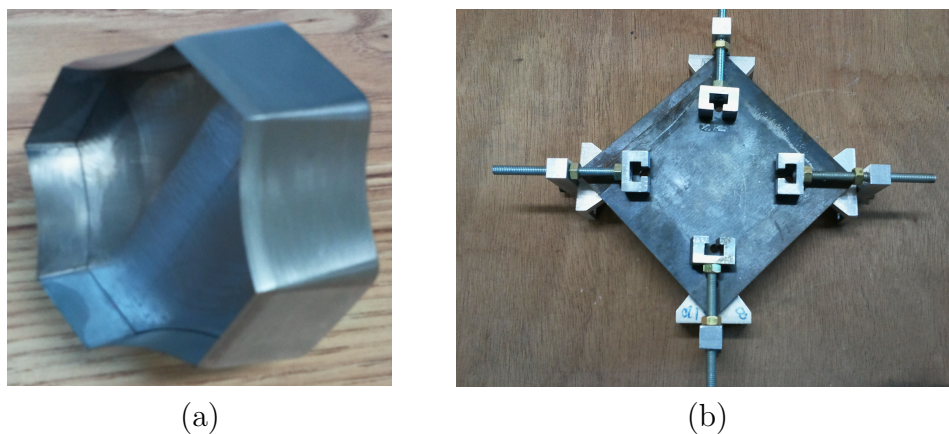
(a) Emporte pièce permettant de découper l'éprouvette à la presse à partir d'une plaque de propergol. (b) Dispositif de collage des mors sur les extrémités de l'éprouvette.
